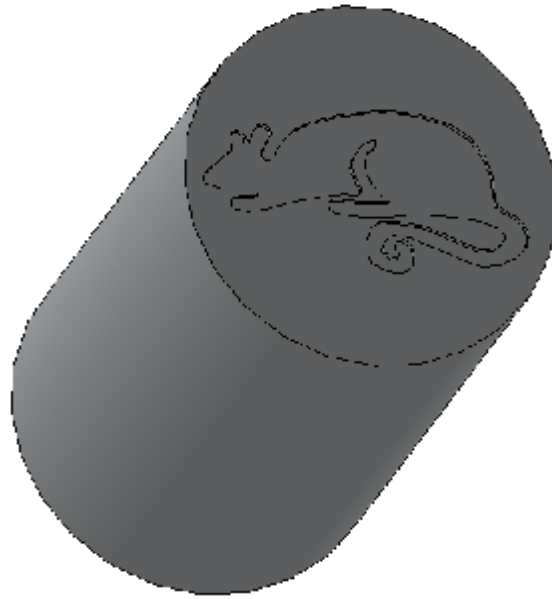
Циліндрична деталь на торці якої заглиблення у формі «пацюка».
